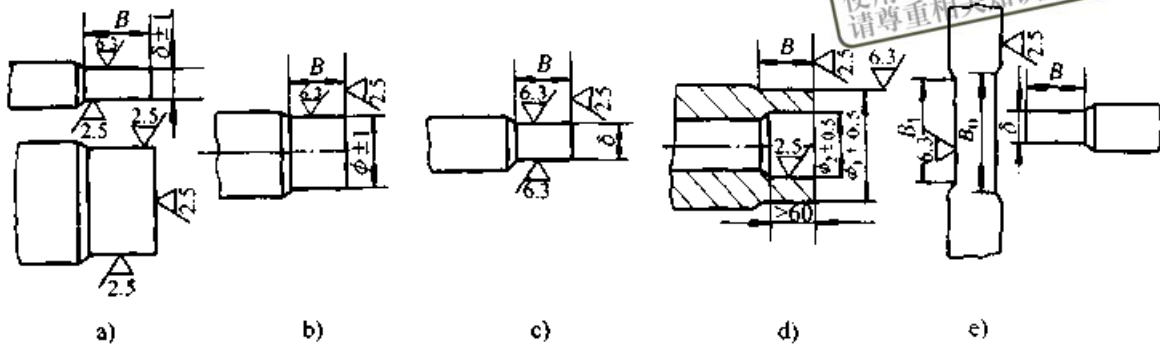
铸、锻件焊接面的加工要求
